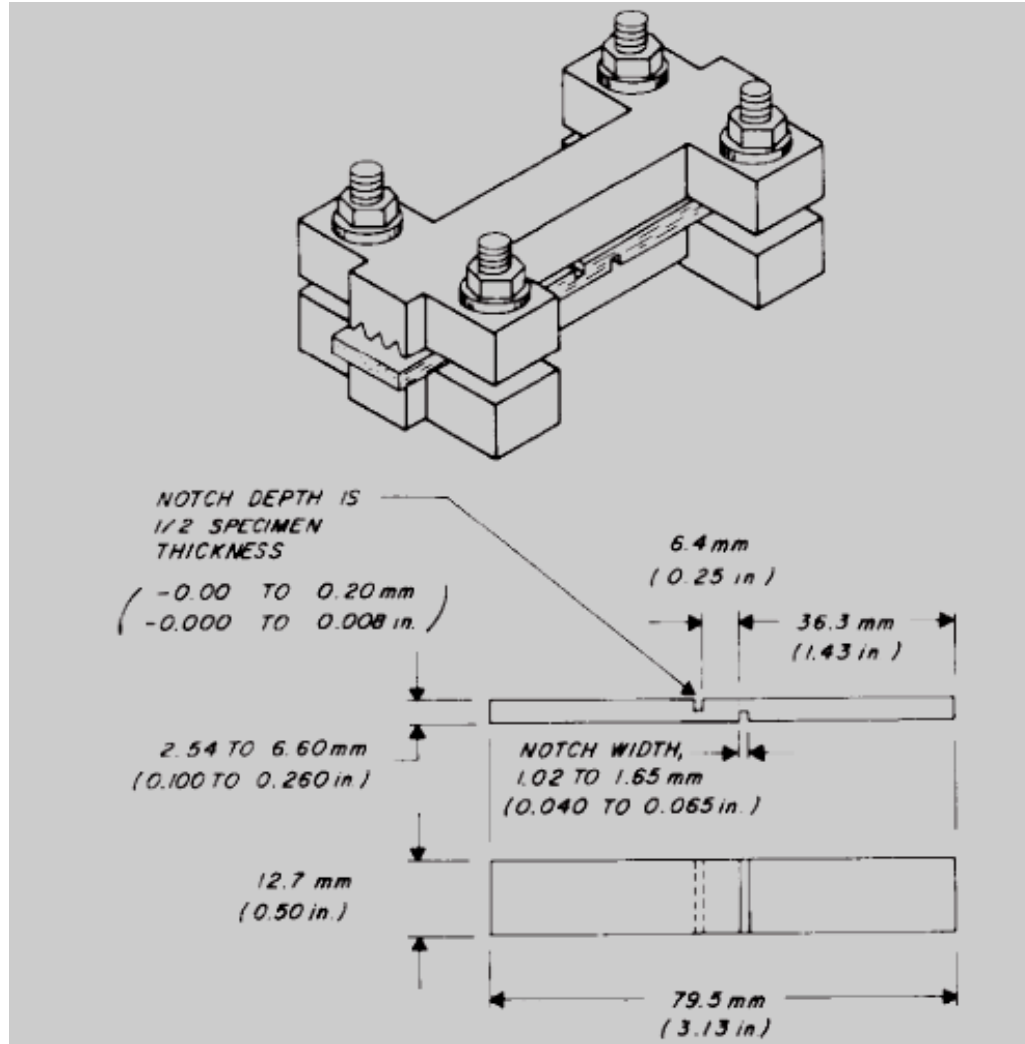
Muestra y plantilla de carga para prueba de cizallamiento en el plano.
